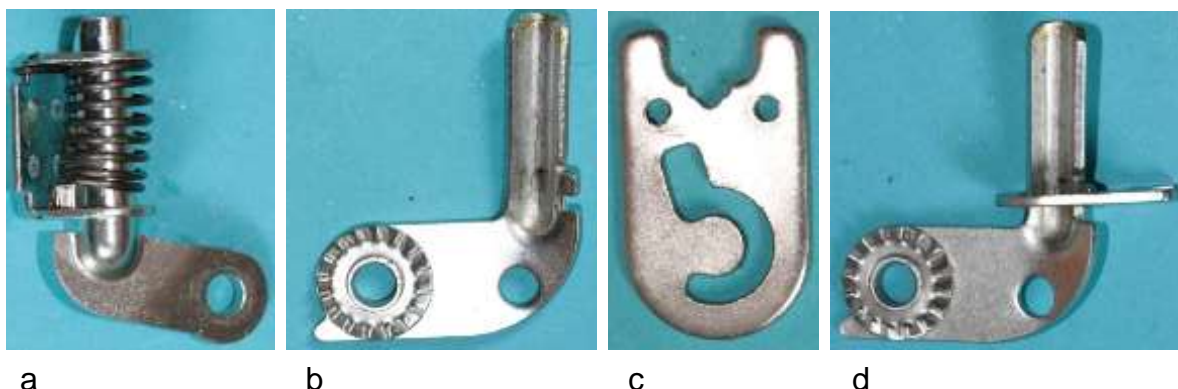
Reduzierung des U-förmigen Basisblechs zu einem flachen Blech, sodass sich die Spiralfeder am Drehbolzen und unmittelbar am Gehäuse abstützt.
